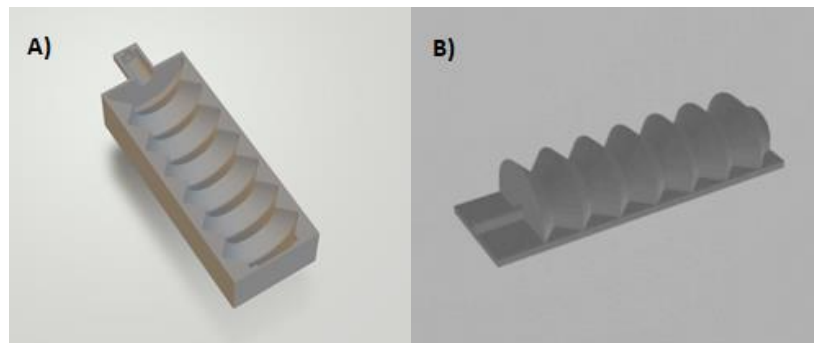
Partes A y B de molde diseñado en SolidWorks guardado en STL
